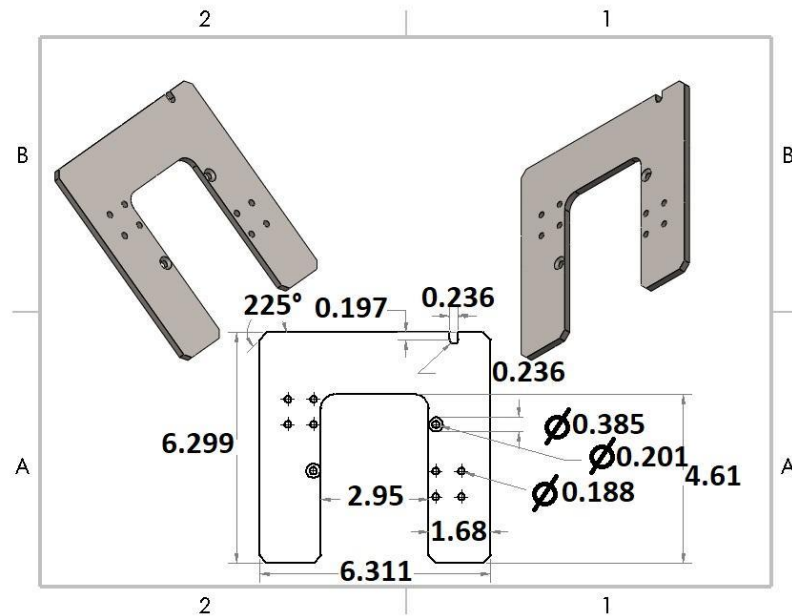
Base de aluminio fabricada por CNC. Las dimensiones están dadas en pulgadas.
